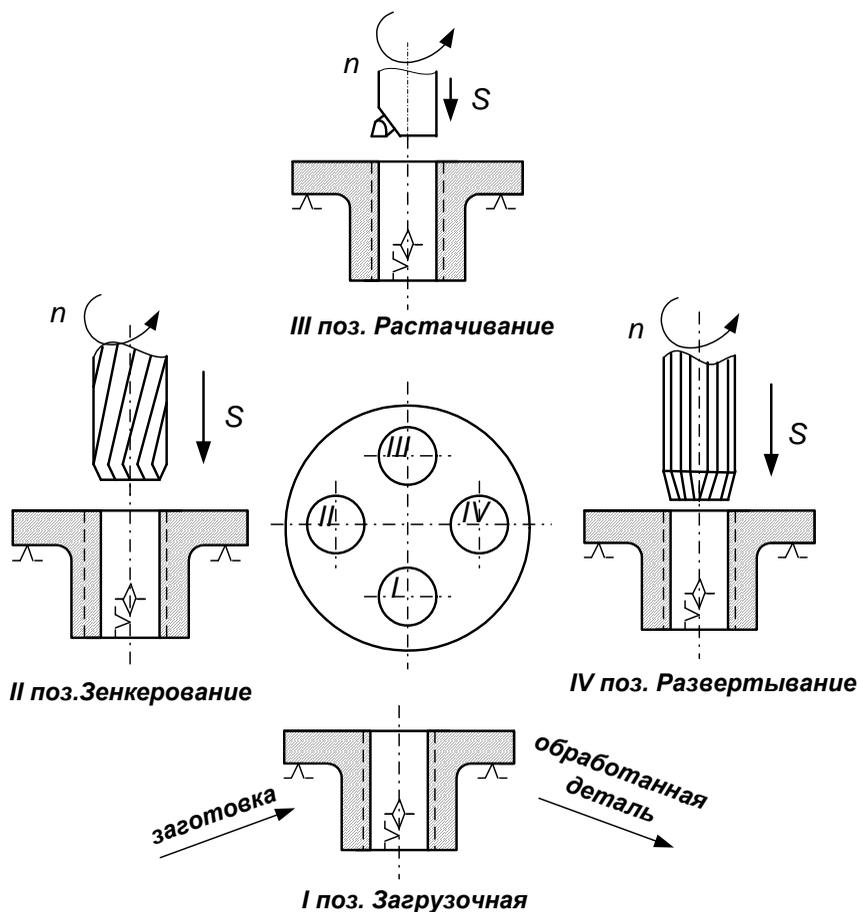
Схема параллельной обработки отверстия одной детали тремя инструментами на 4-х позиционном станке
